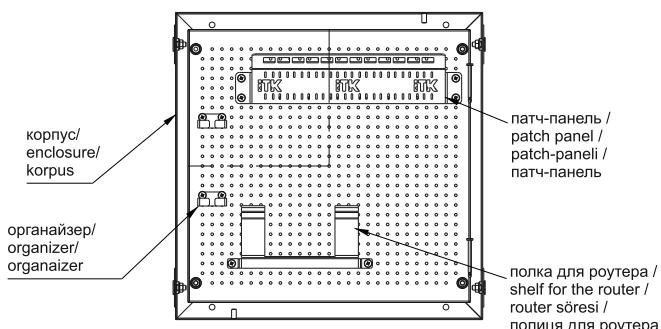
Корпус / Figure 2 – Enclosure / 2-suret – Корпус
